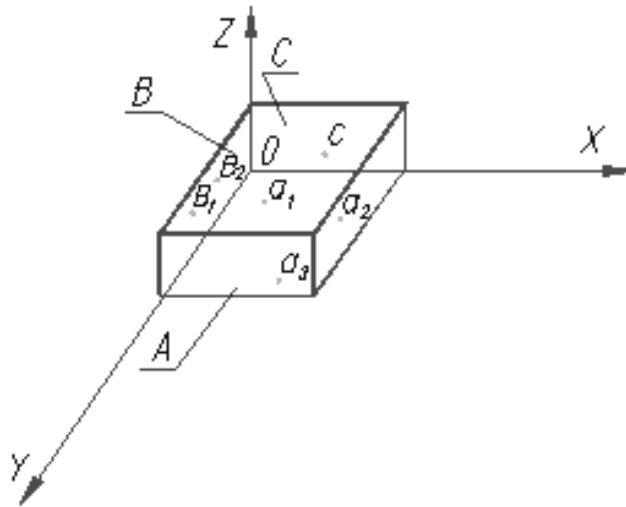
Схема расположения призматической заготовки в пространстве.
